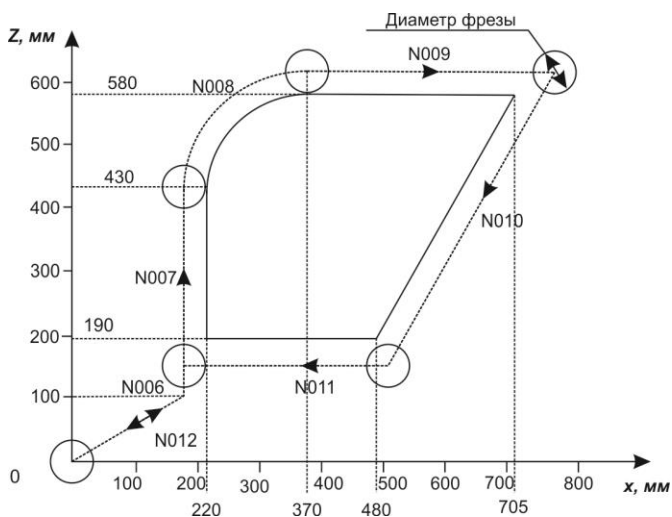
Движение фрезы по эквидистанте при фрезеровании
